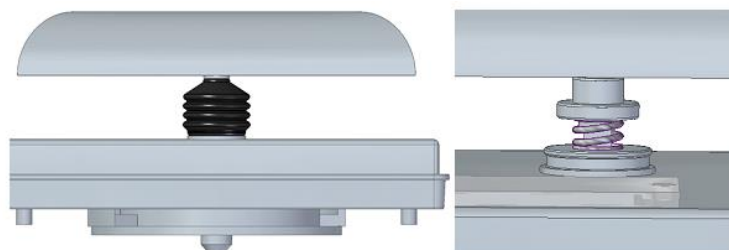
Montaje fuelle-muelle Prot. 1 en CAD
